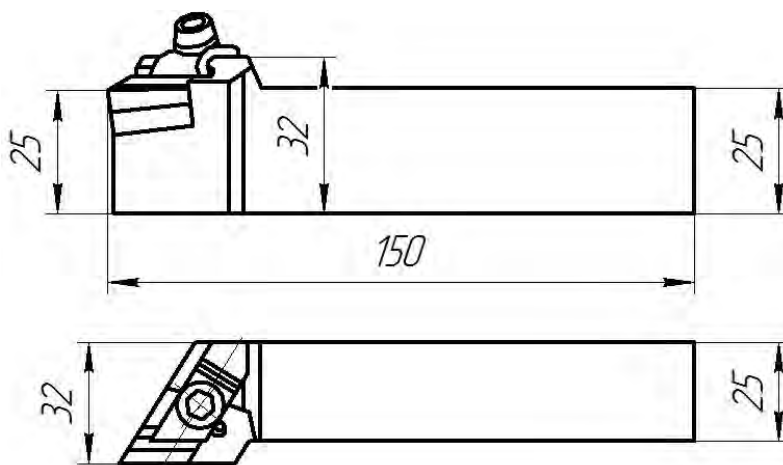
Резец контурный сборный по ГОСТ 20872-80
